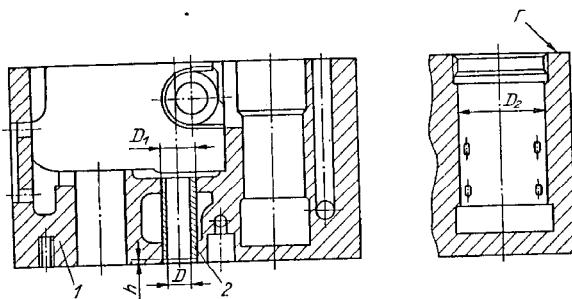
Корпус 1 средний в сборе /рис. 129/
